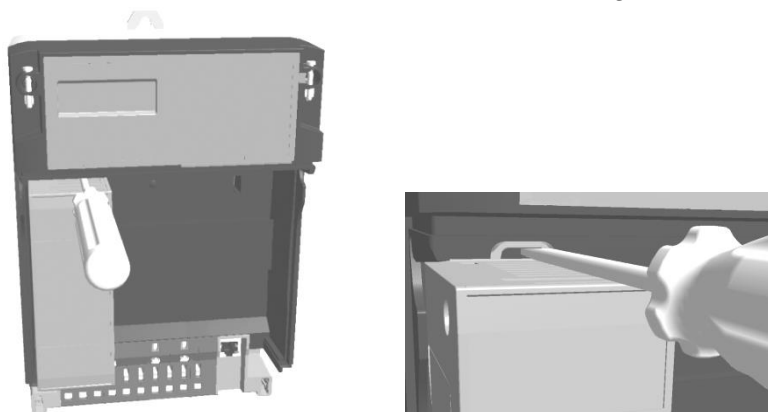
Module durch leichtes Drehen des Schraubendrehers entriegeln
